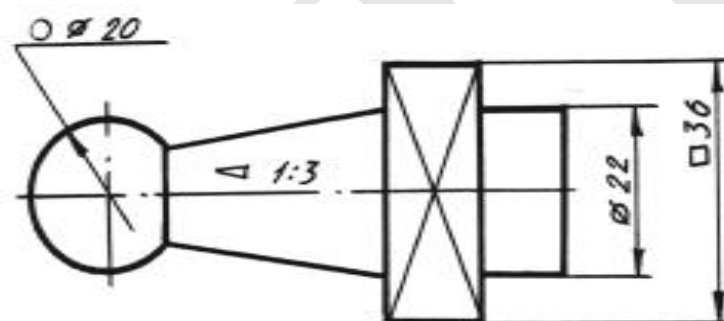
Пример простановки размеров (сфера, конус, квадратная призма, цилиндр)
